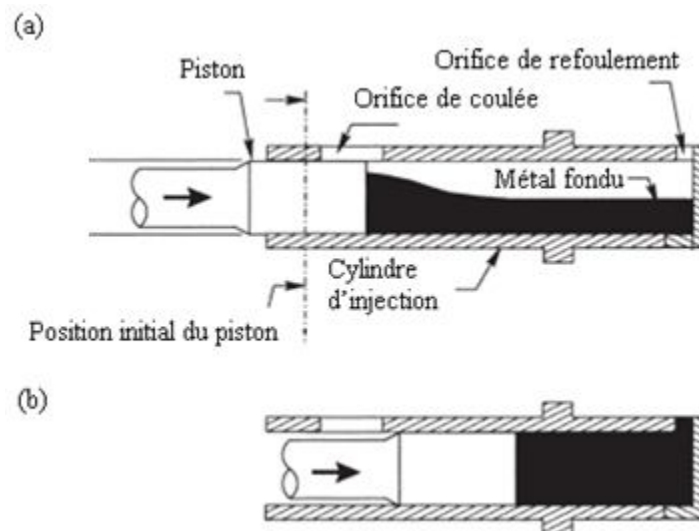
Cylindre d'injection horizontale d'une machine de MMSP :
